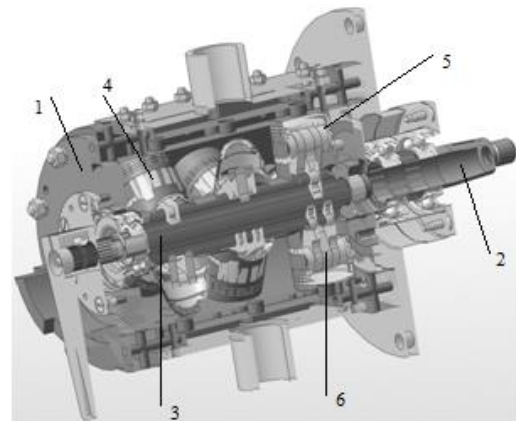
Роторно-поршневий двигун 12РПД-4,4/1,75 [7]: 1 – корпус; 2 – ротор; 3 – кулачок; 4 – поршень; 5 – поршневий палець; 6 – рухома ланка
